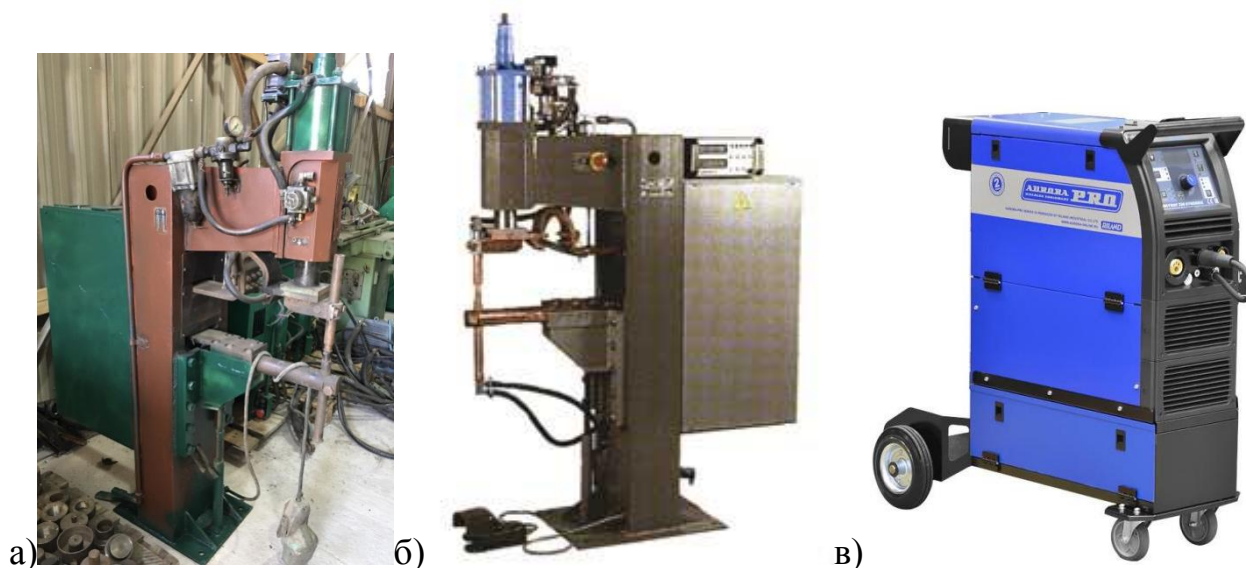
Машина для контактной рельефной сварки крепежных элементов МТ-1621 (а) и контактной точечной сварки листовых элементов МТ-1928 (б), полуавтомат Aurora PRO Skyway-30 (в)
